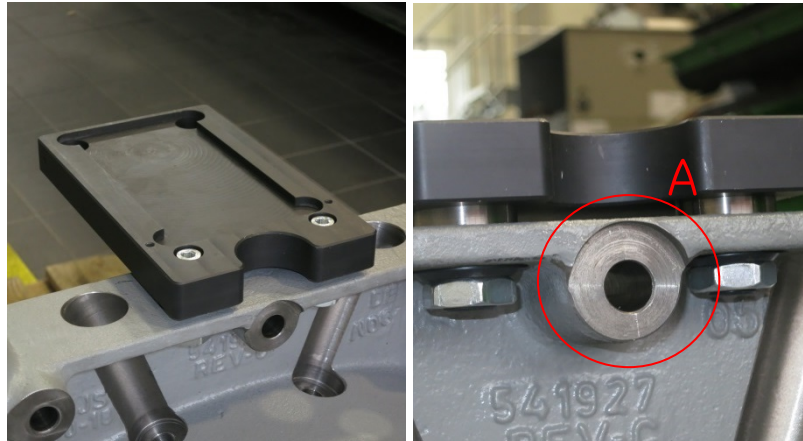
u 24: Ansichten aufgespannter Vorrichtung für BP1
